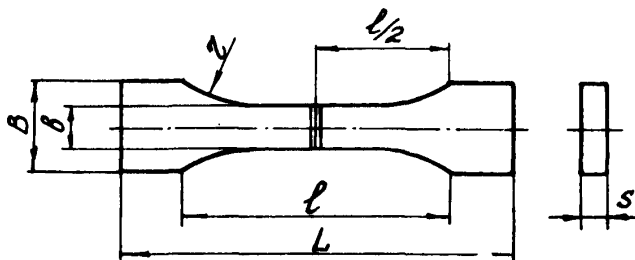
Образец для испытания сварных стыковых соединений на растяжение
